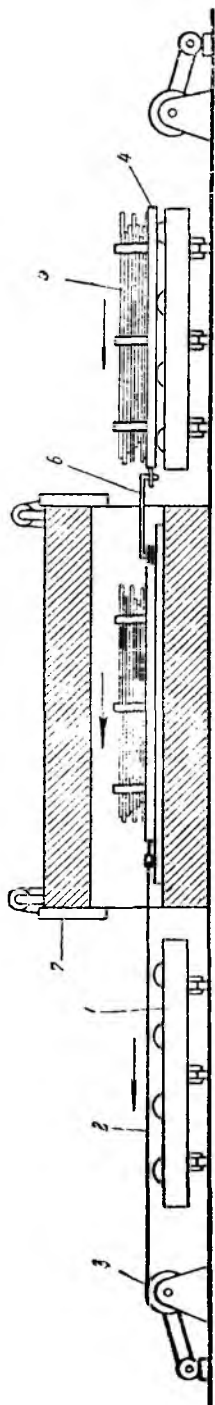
Схема устройства отжигательной печи с загрузочными приспособлениями.
